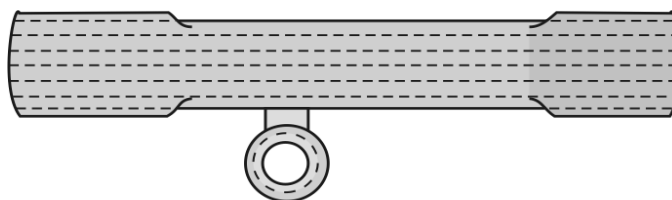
Схема сканирования кронштейна и боковых поверхностей подвески тормозного башмака
